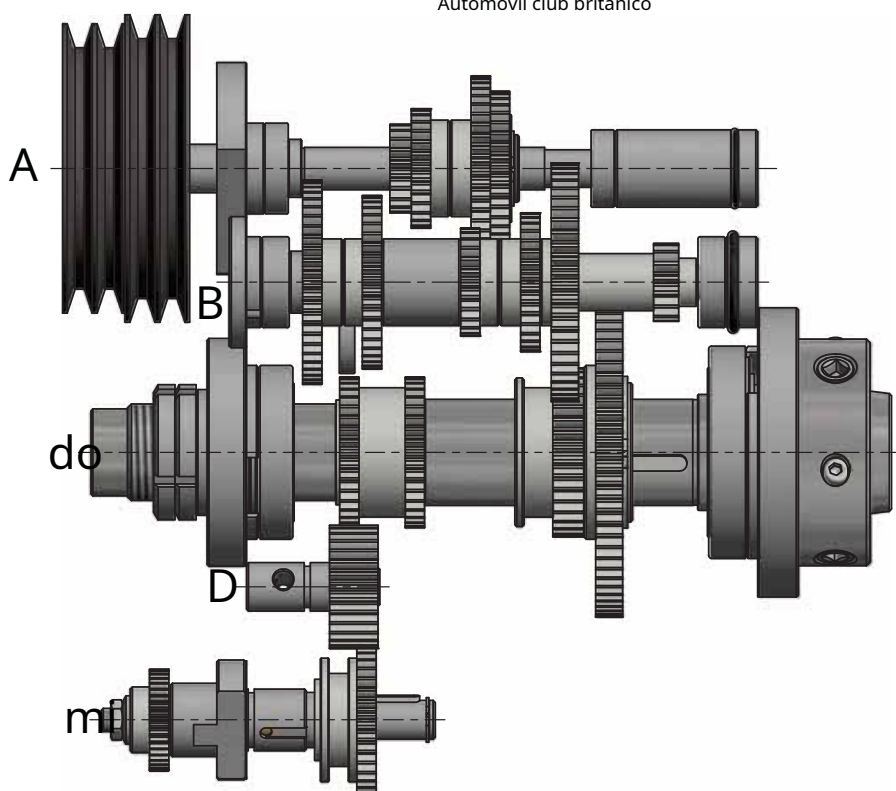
Getriebe Spindelstock 2-6 - Engranaje del cabezal 2-6
